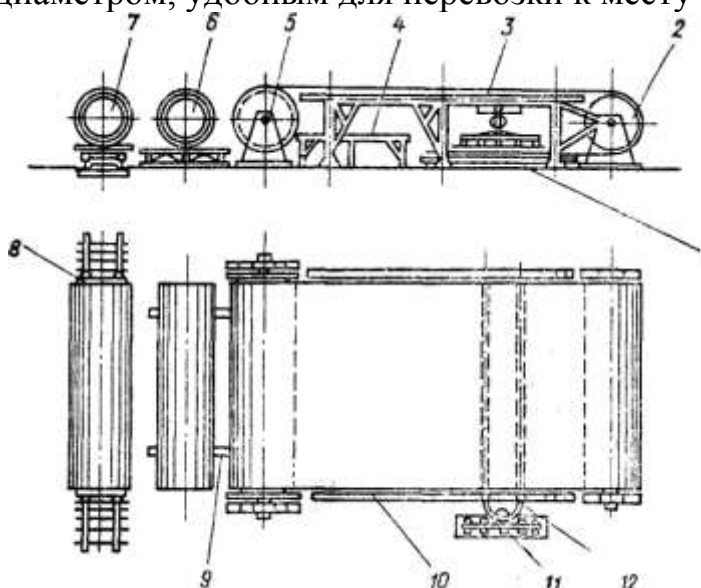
Схема двухъярусной установки для изготовления сварных листовых полотнищ методом рулонирования
